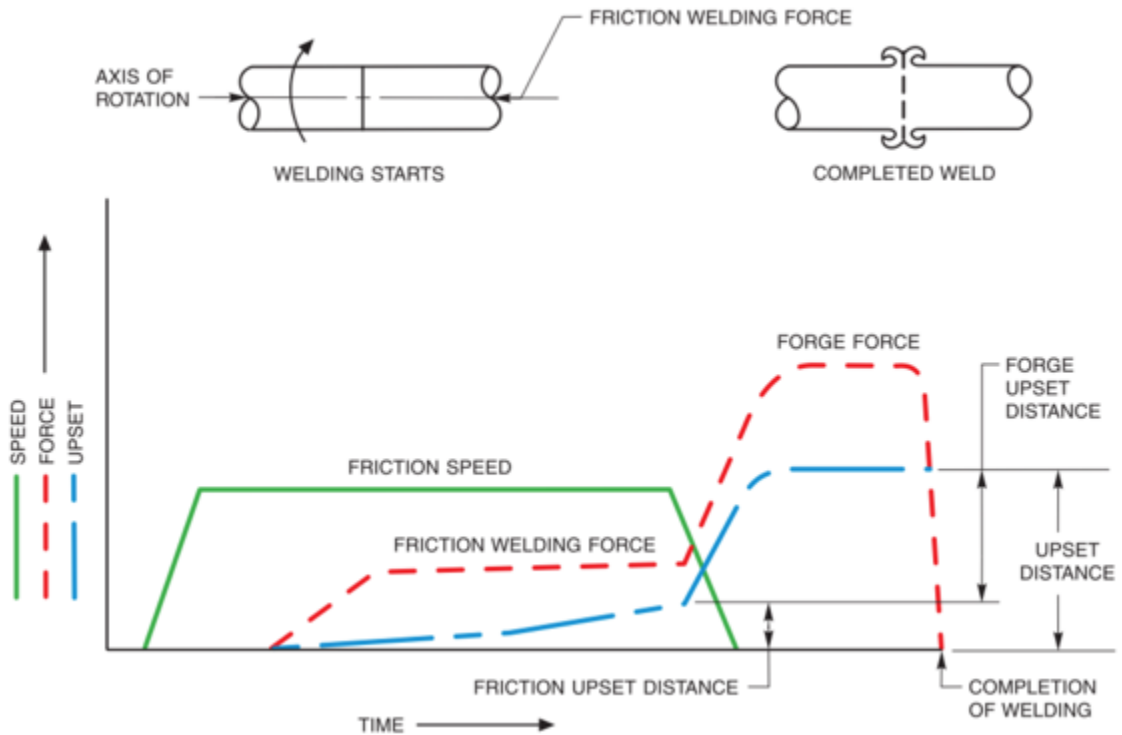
Características y parámetros de la soldadura por fricción directa
